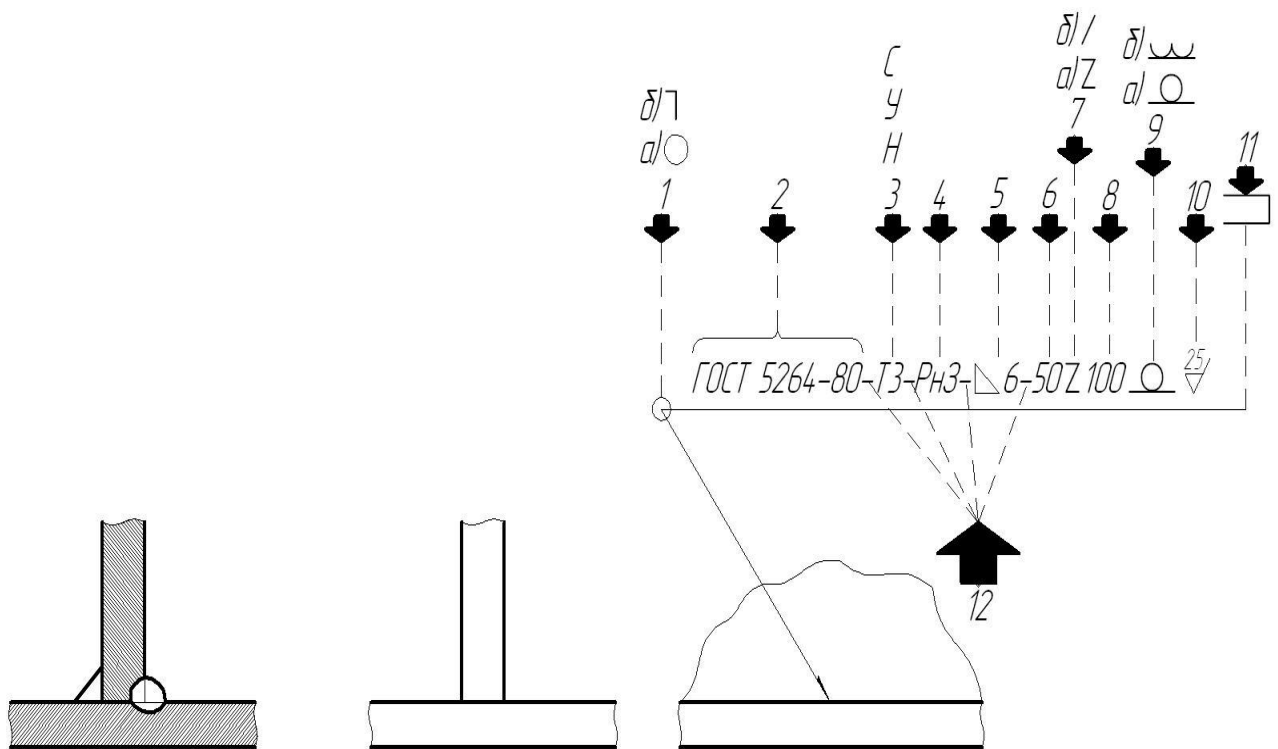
Структура обозначения шва сварного соединения (сварка плавлением):
